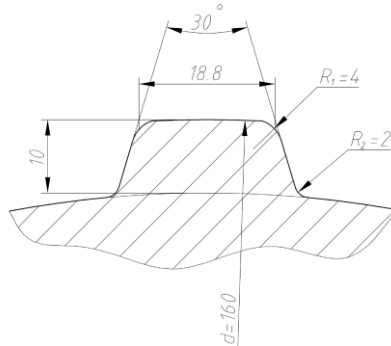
Конструктивне виконання шліца подаючого механізму установки для розрізання конвеєрної стрічки
